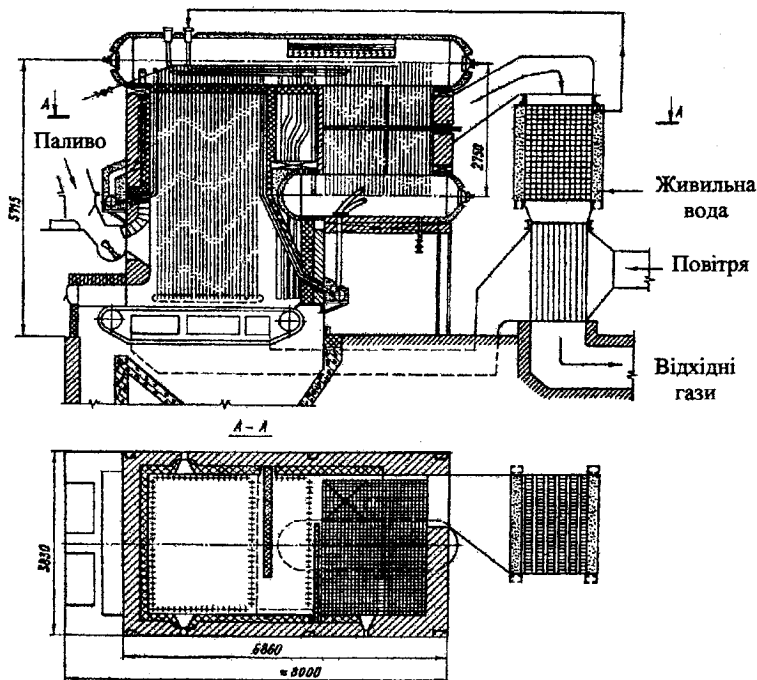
Схема котлоагрегату з горизонтальними газоходами
